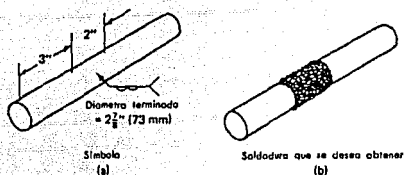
Soldadura de revestimiento, con sus dimensiones particulares.
